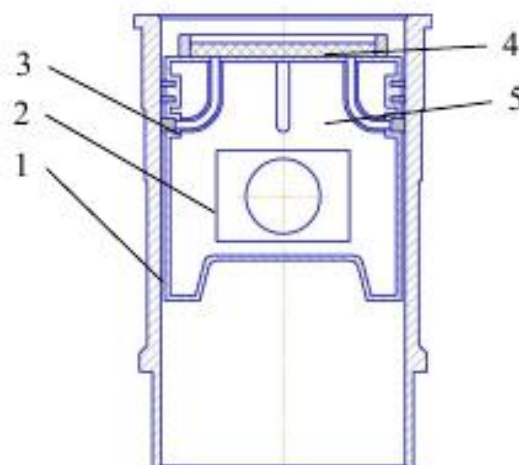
Схема змащування робочої поверхні гільзи циліндра
